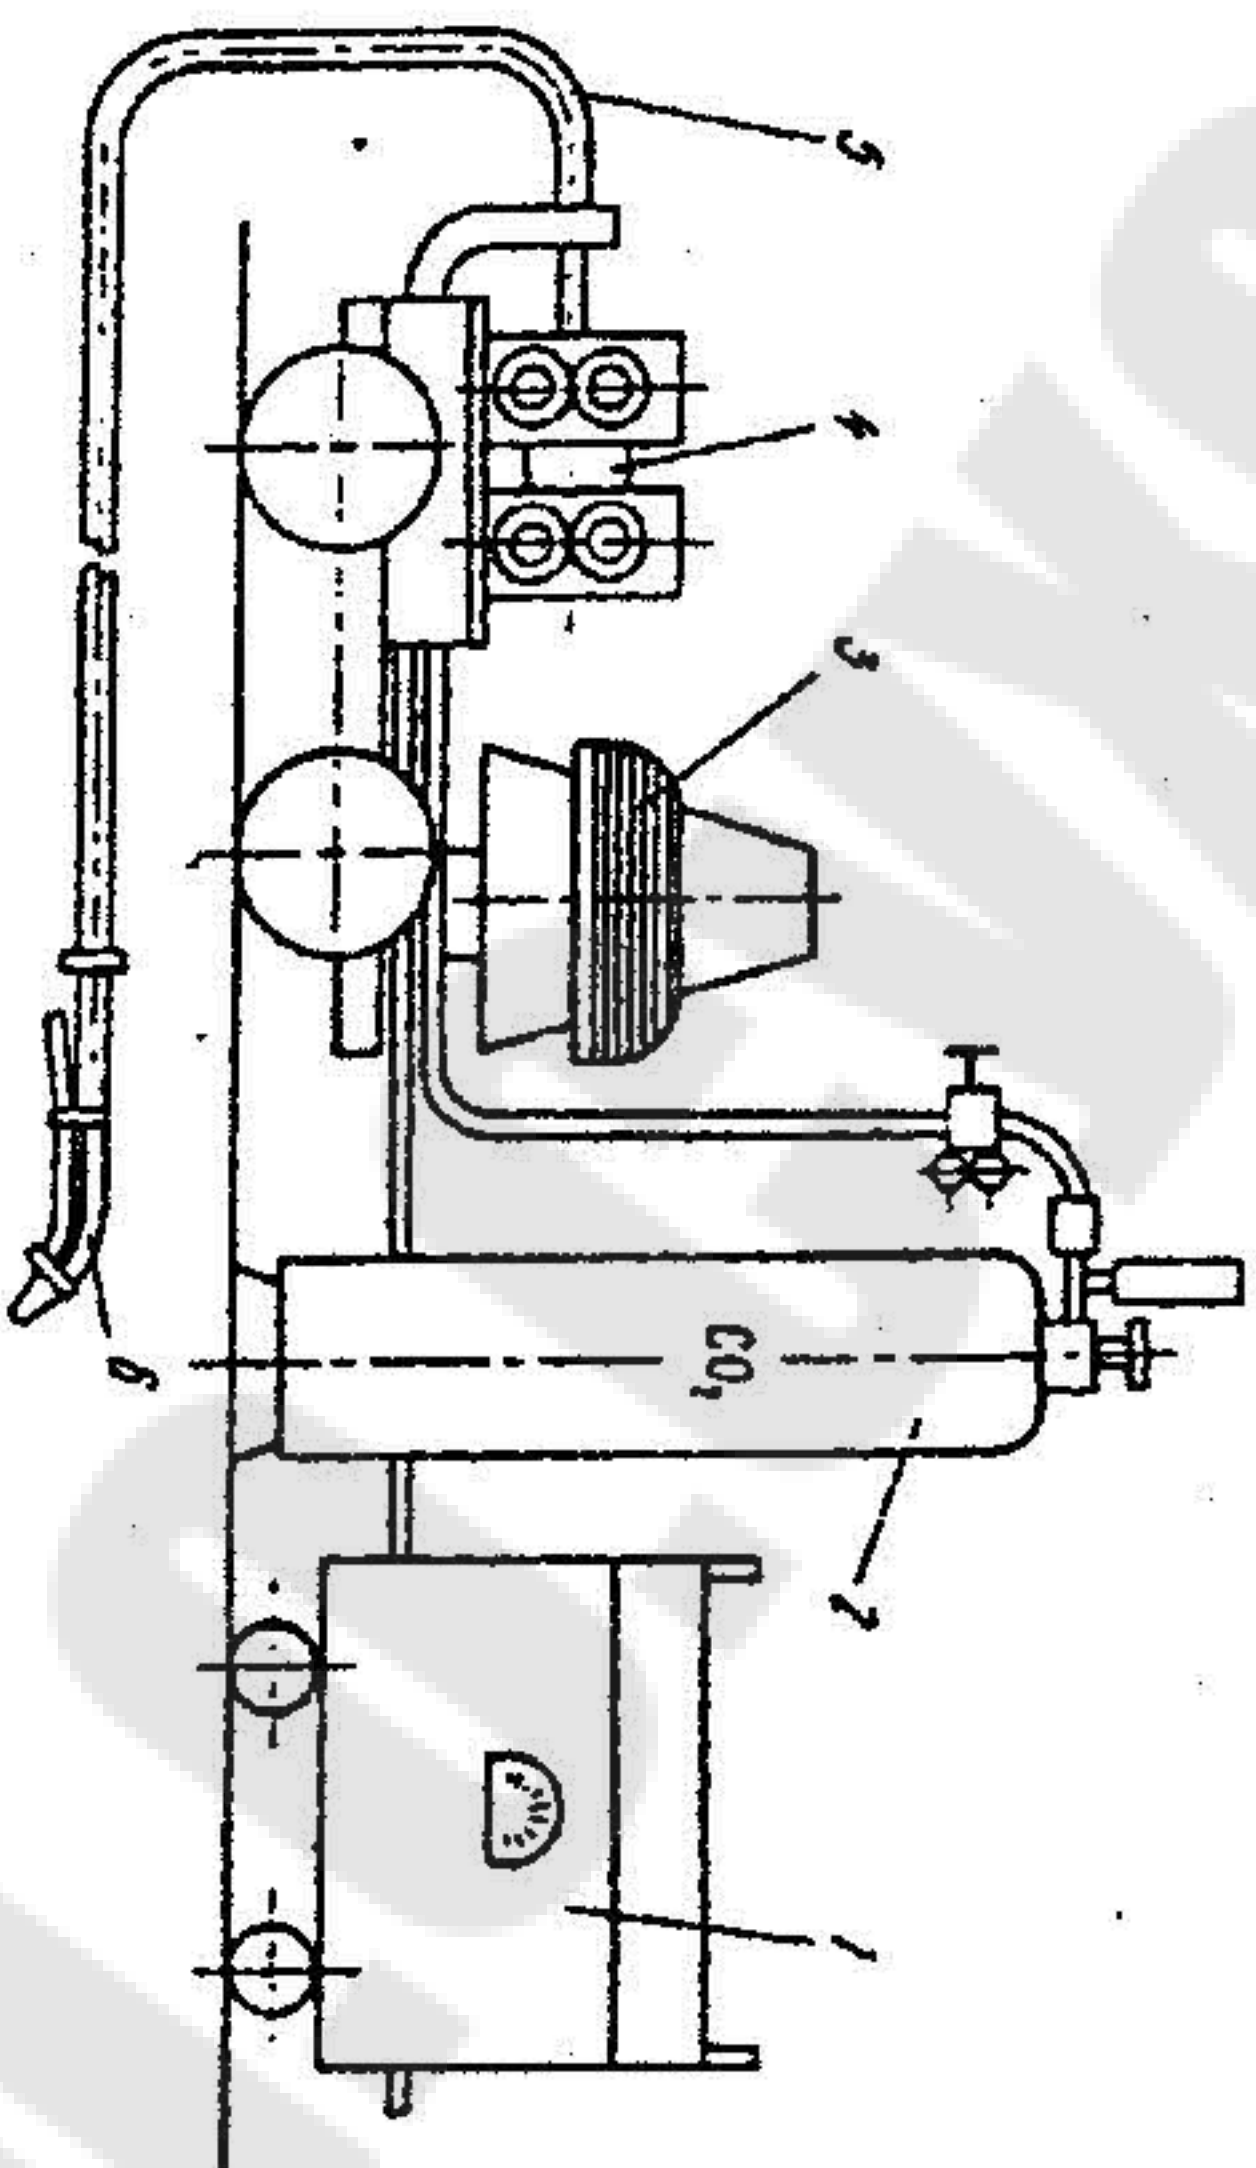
Схема полуавтоматического аппарата для наплавки деталей в среде углекислого газа: 1 - источник питания; 2 - баллон с защитным газом; 3 - бухта проволоки; 4 - подающий механизм; 5 - гибкий шланг; 6 - горелка
